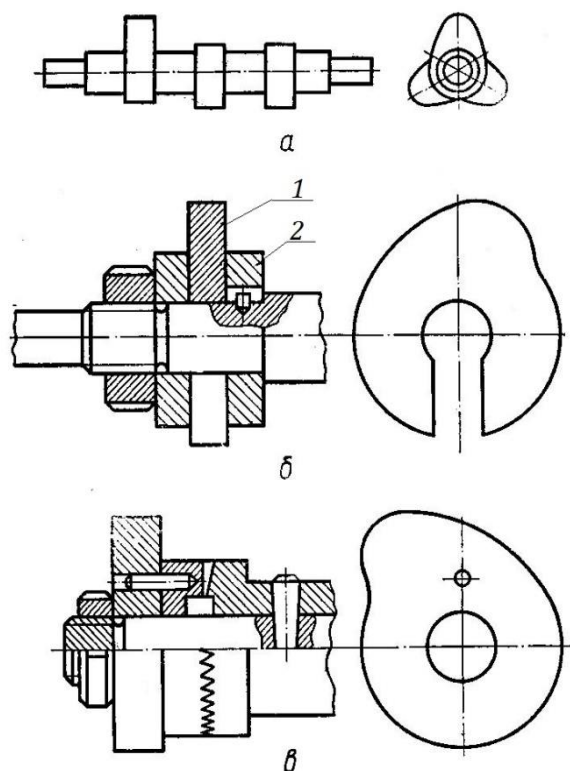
Кулачки: *а* – изготовлен заодно с валом;
